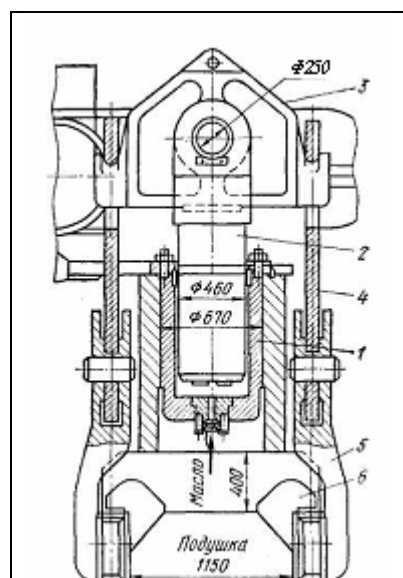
Устройство гидравлического уравнивания верхнего опорного валка с подушками (четырёх-валкового стана 2500 конструкции НКМЗ) при помощи одного верхнего цилиндра
